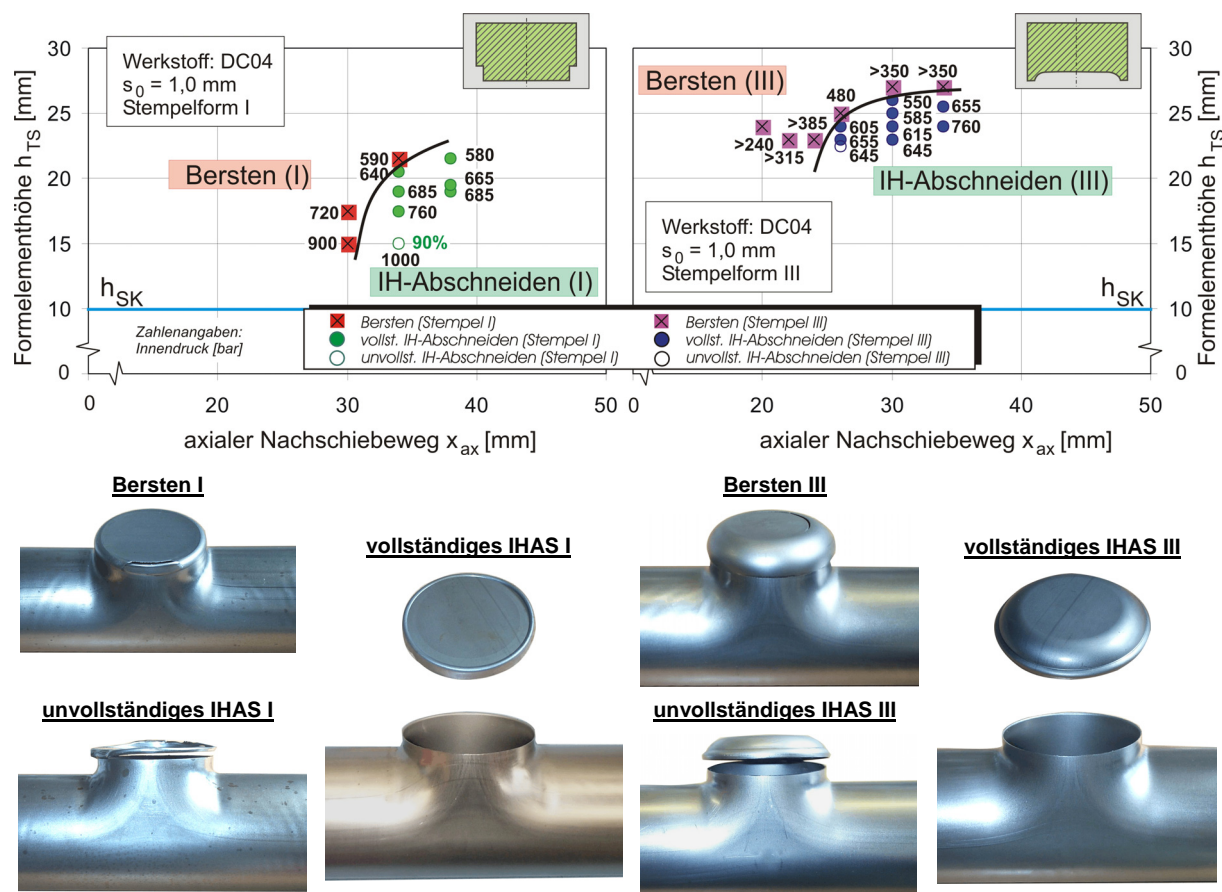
Prozessfenster und Beispielteile für das IH-TAS (DC04; 1,0 mm; Stempelformen I und III)
